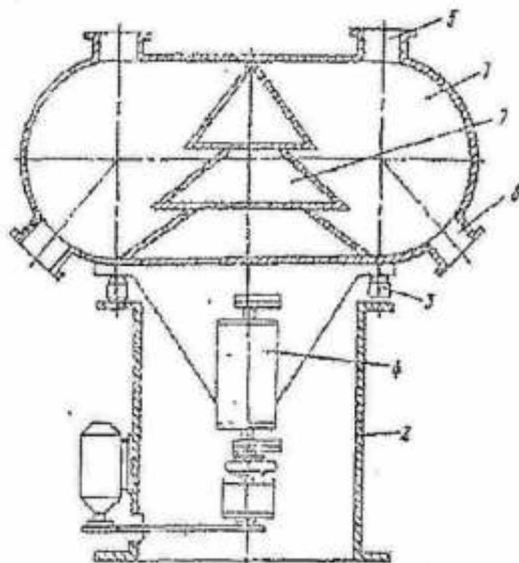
Вібраційний змішувач з тороподібною камерою змішування
